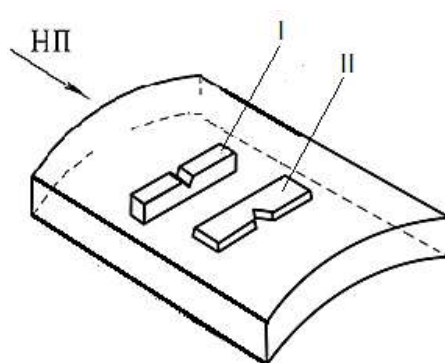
Схема вырезки образцов для испытаний на ударный изгиб
